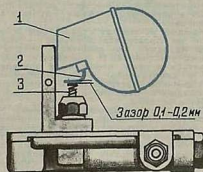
Проверка зазора между демпфирующей пружиной 3 и язычком 2 поплавка 1.
